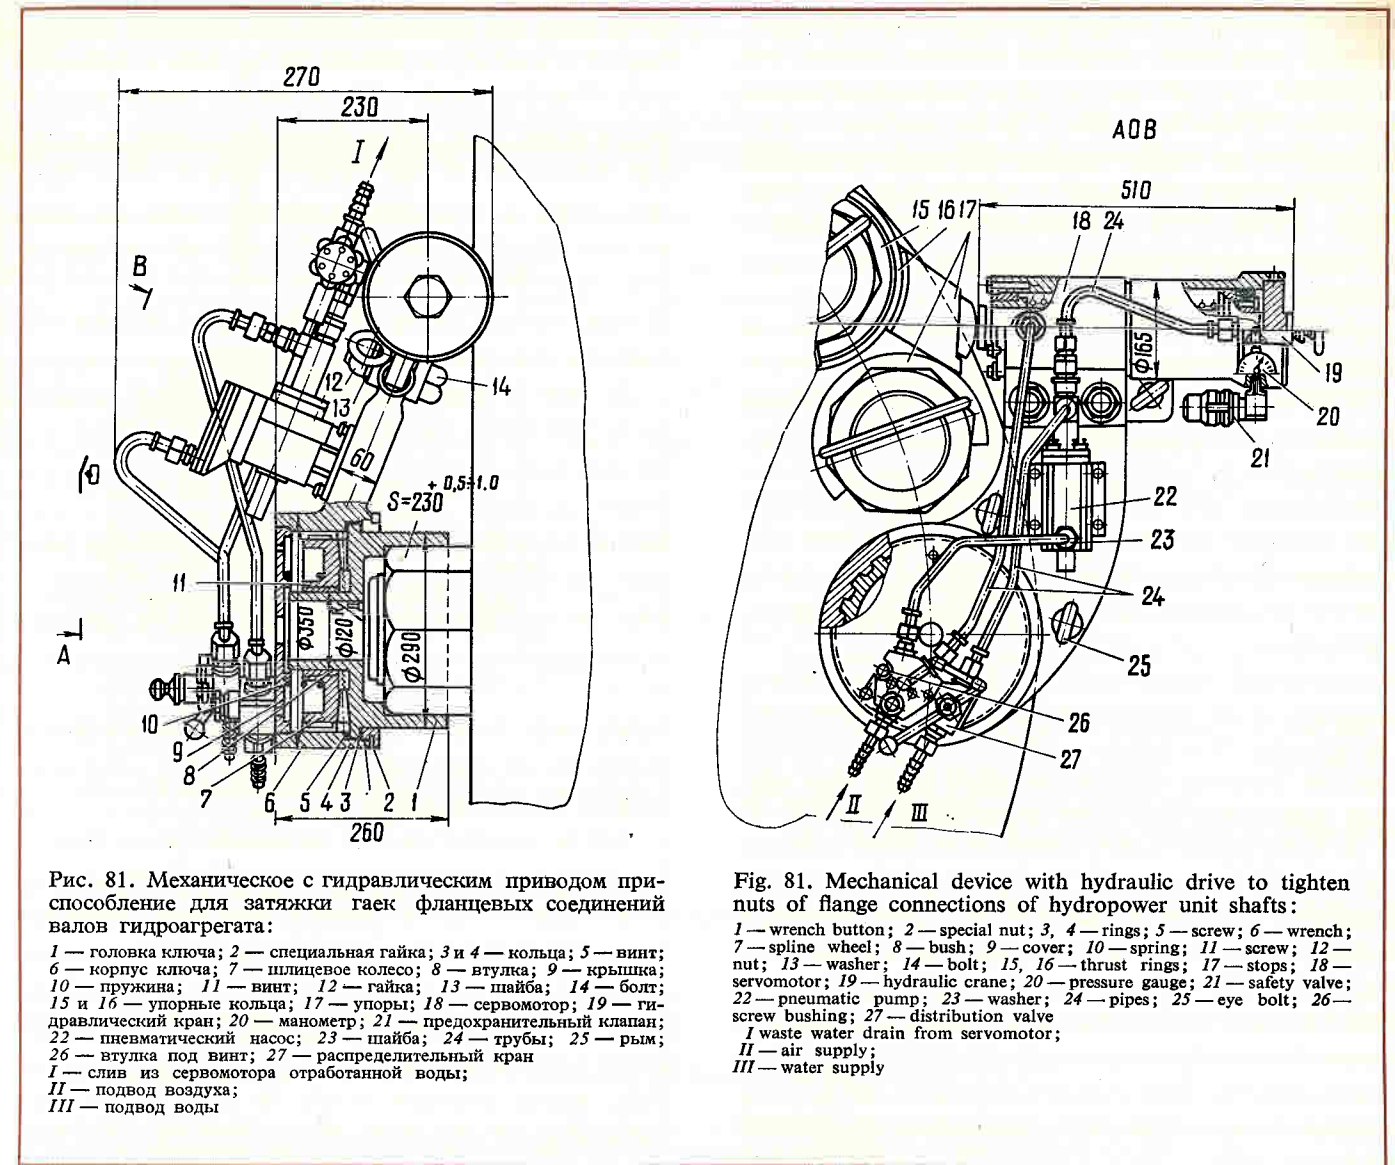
Механическое с гидравлическим приводом приспособление для затяжки гаек фланцевых соединений валов гидроагрегата:
